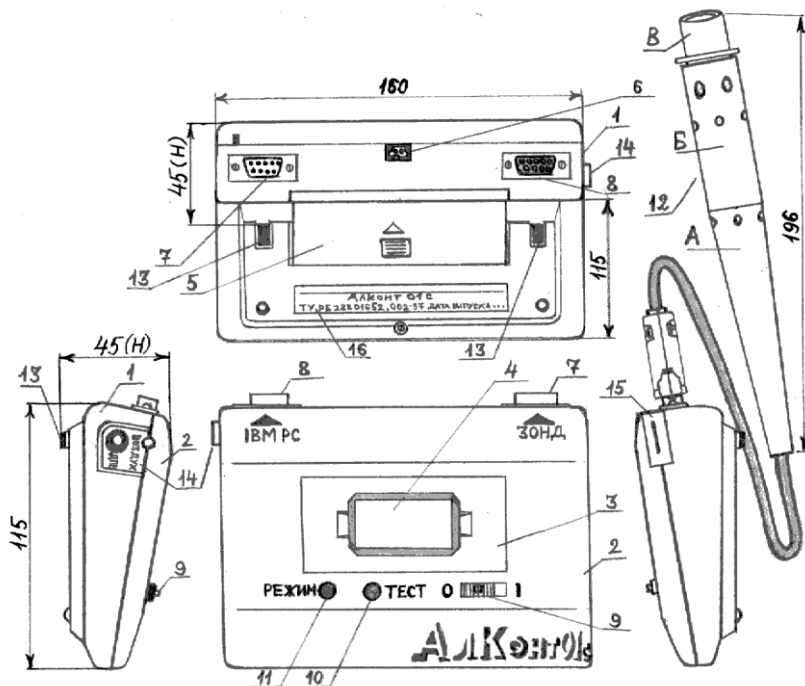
Внешний вид и габаритные размеры прибора "Алконт 01с".
